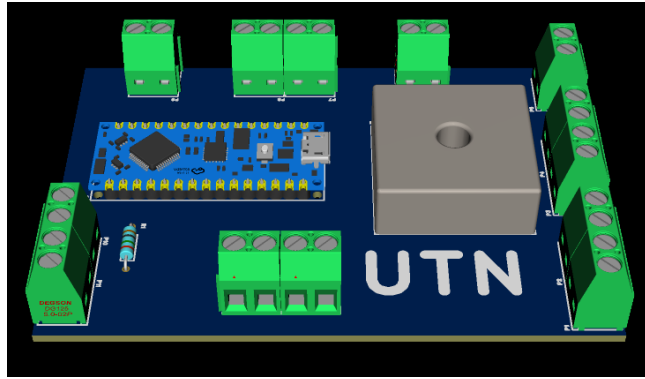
Diseño en 3D del PCB en EasyEDA.
